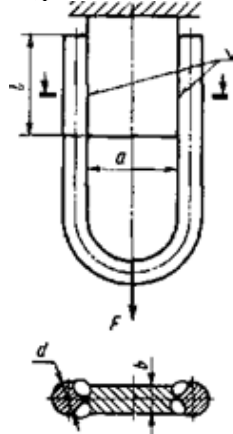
Сварное соединение узла подвески металлоконструкции
